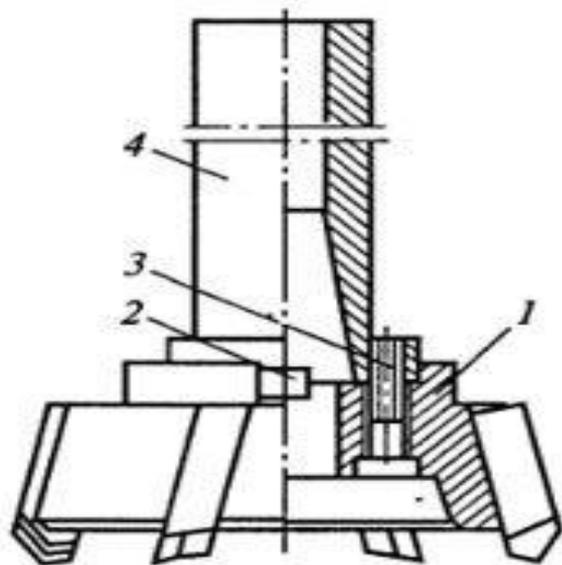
Установка торцовых насадных фрез на шпиндель станка:
